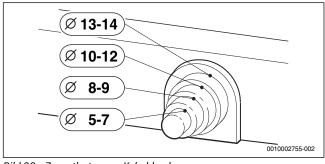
Zugentlastung an Kabeldurchmesser anpassen
